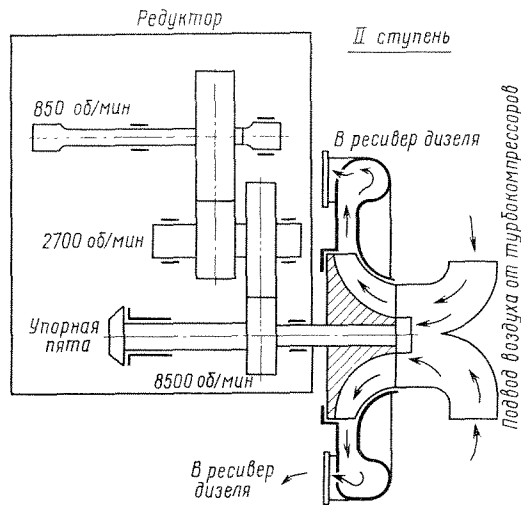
Схема приводного центробежного компрессора дизеля 10Д100
